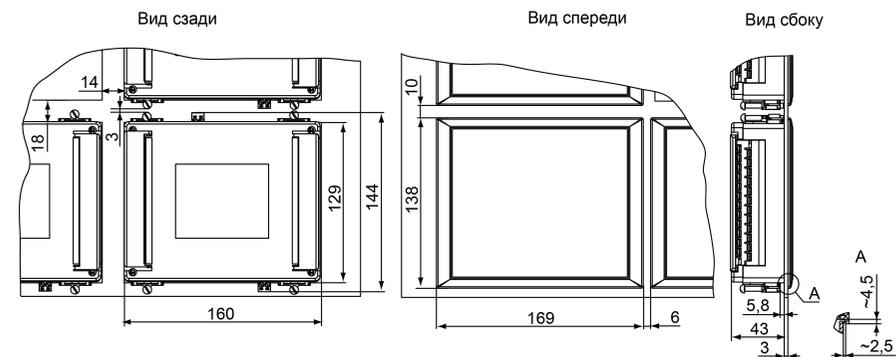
Прибор в корпусе Щ7, установленный в щит толщиной 3 мм
